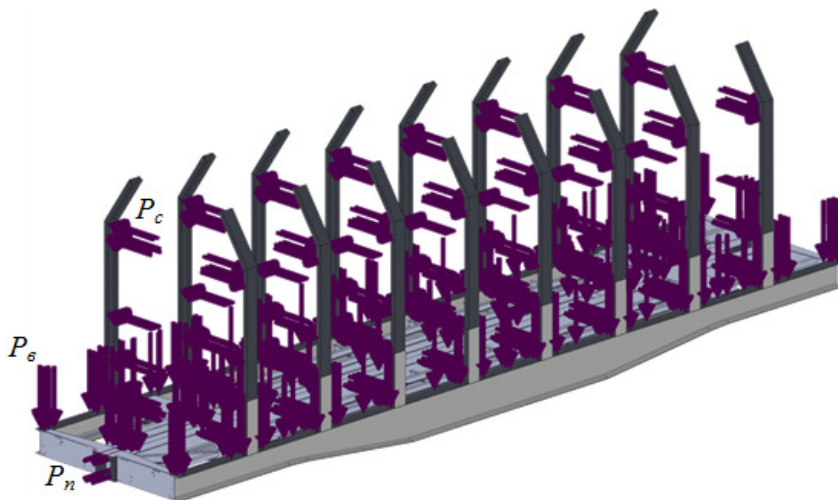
Розрахункова схема несучої конструкції вагона-платформи
